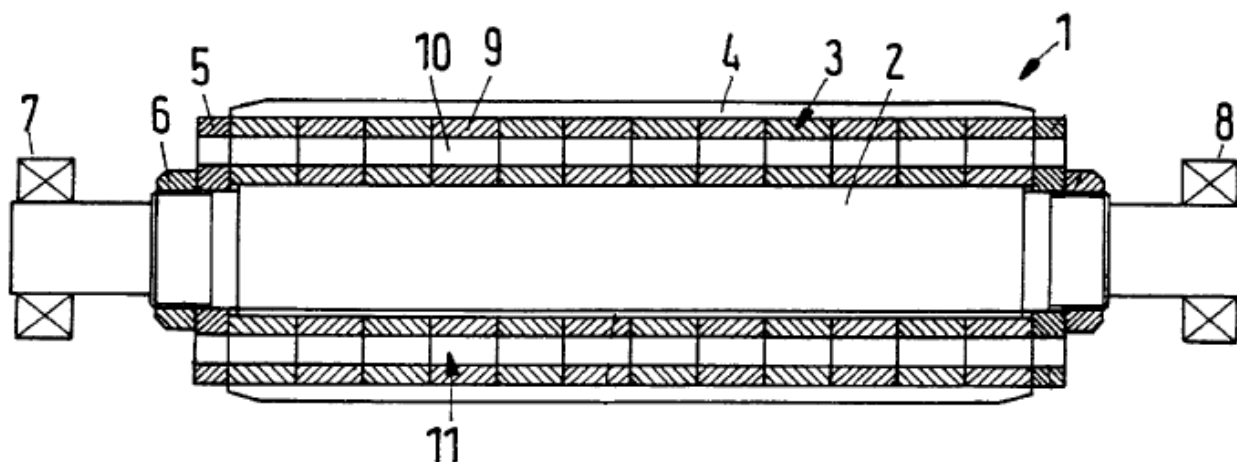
Загальний вид валка каландра в поздовжньому розрізі: 1– каландровий вал;
